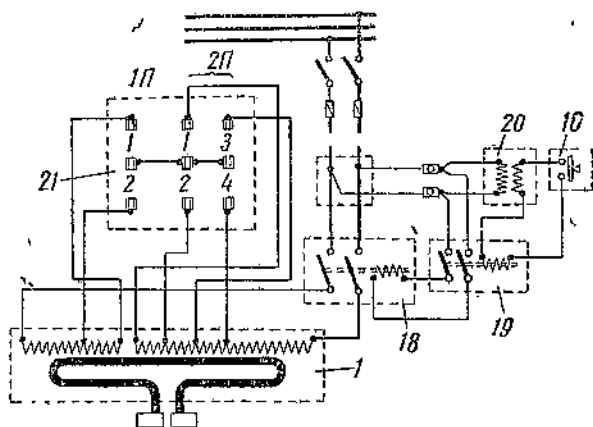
Машина для стыковой сварки АСА-100.
